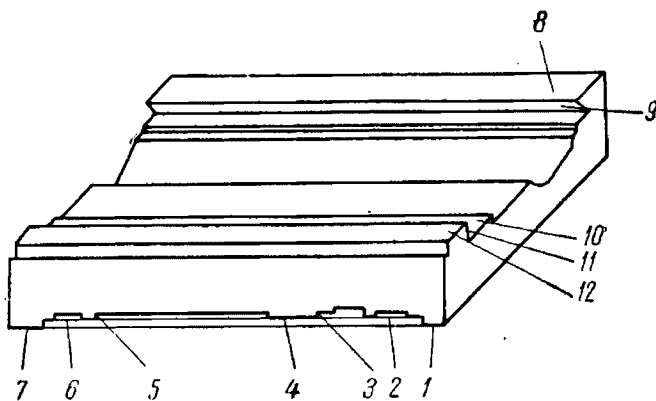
Направляющие каретки стола шлиф-фрезерного станка
